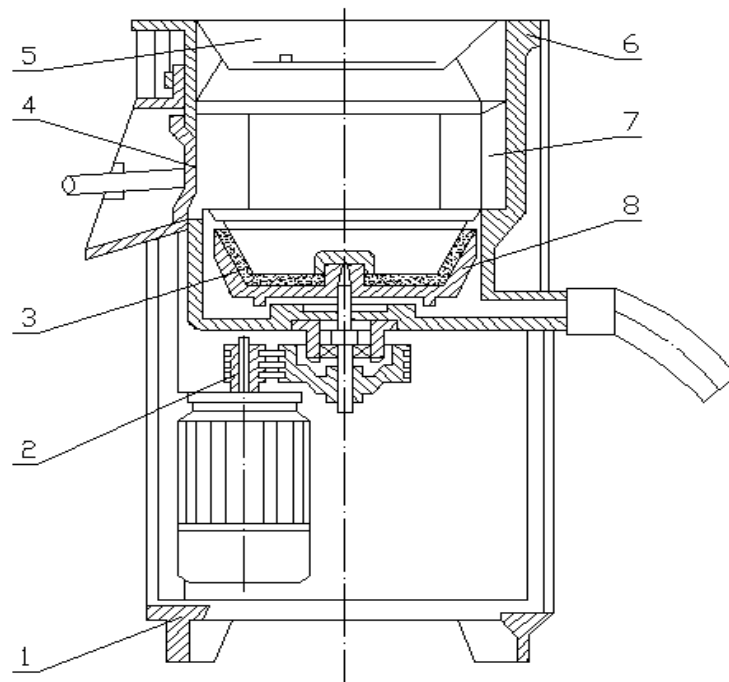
Схема картоплеочищувальної машини типу МОК: 1 – основа машини; 2 – привод; 3 – чаша; 4 – розвантажувальні дверцята; 5 – кришка для завантаження; 6 – корпус робочої камери; 7 – сегменти; 8 – конус
